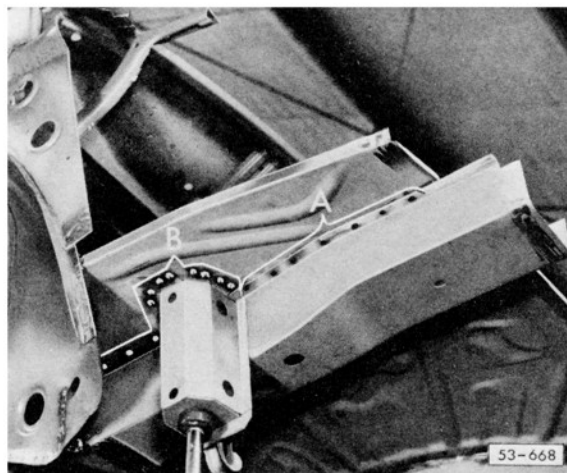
Kofferboden hinten – Teilstück einschweißen.
